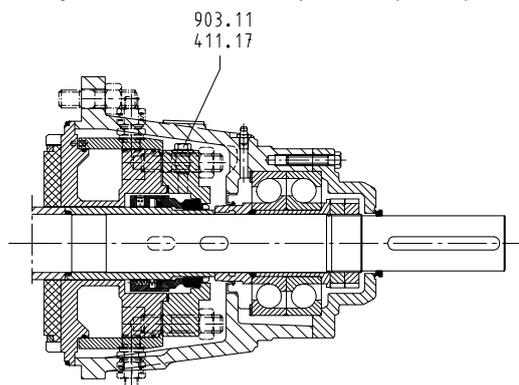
Пробка выпуска воздуха из камеры уплотнения (корпус уплотнения с водяным охлаждением) — типоразмеры 125–150 (и при необходимости для типоразмеров 32–100 как специальное исполнение)
